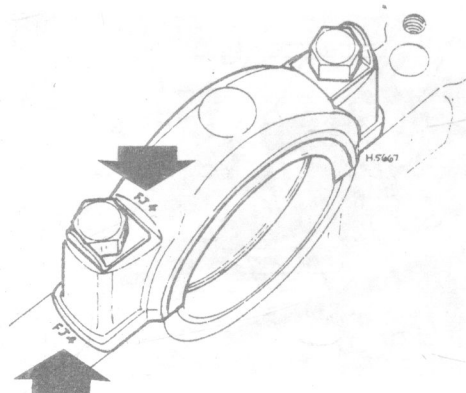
Номера коренных подшипников коленчатого вала (см. раздел 41)
